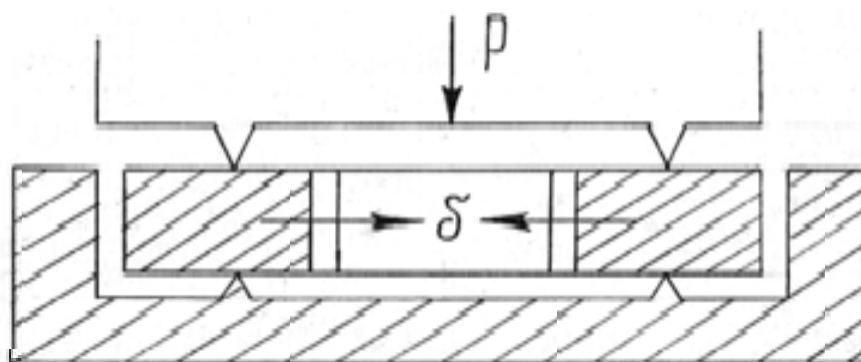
Восстановление вдавливанием гайки подшипников задних колёс при износе резьбы
